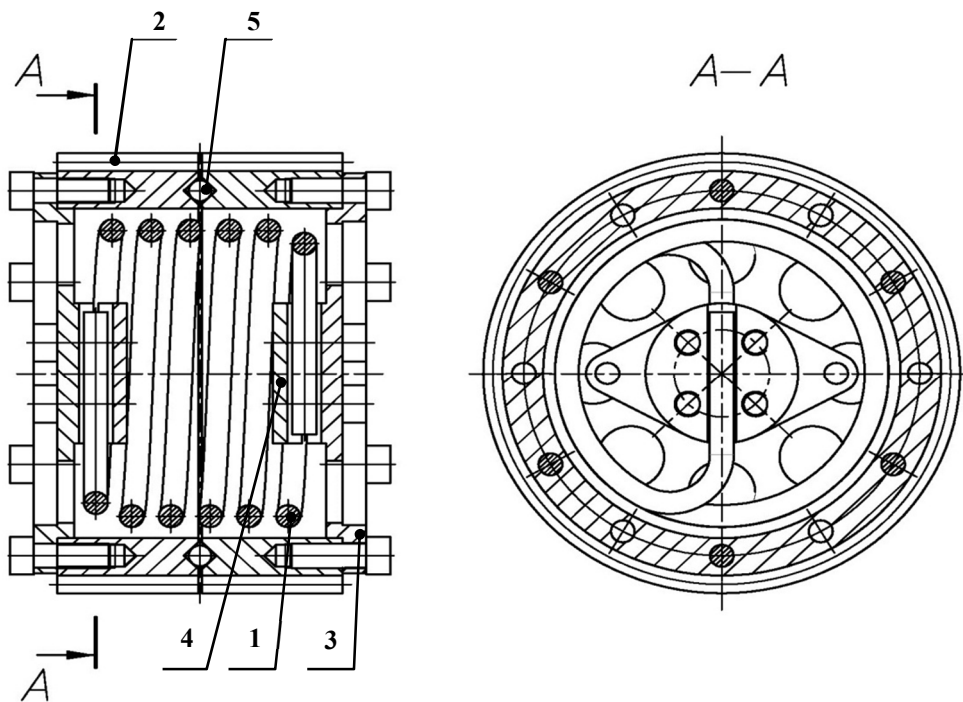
Сателлит: 1 – пружина; 2 – шестерня; 3 – фланец; 4 – фиксатор; 5 – насыпной подшипник
